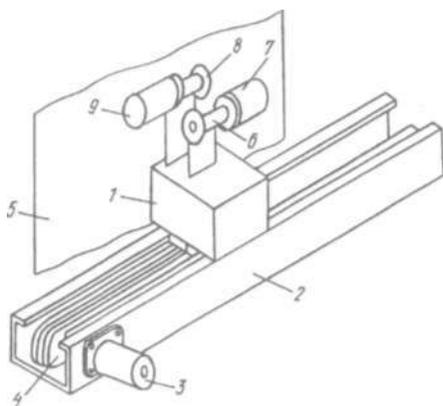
Устройство для маркировки и отметки пороков. Патент 3436231, Германия
